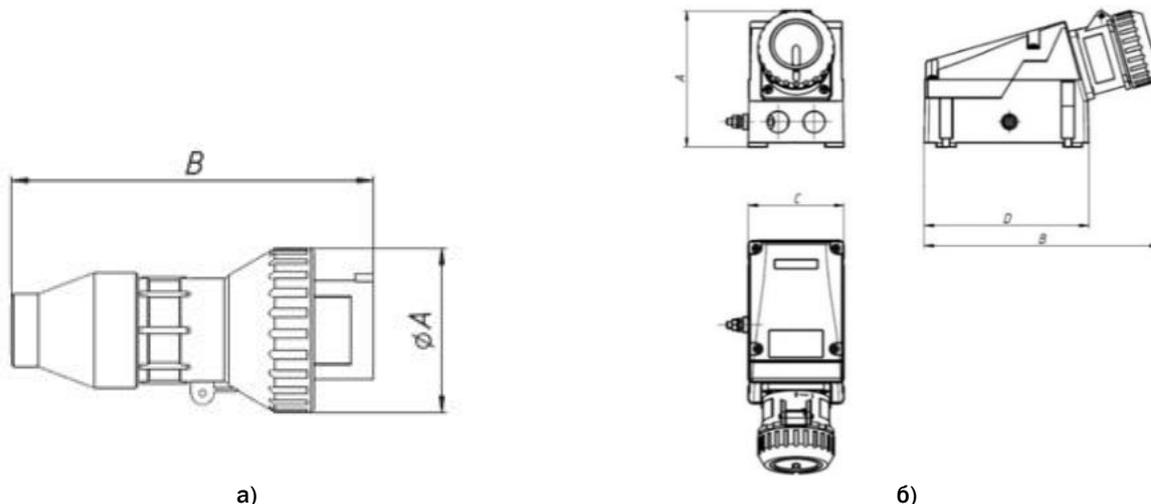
а - Общий вид вилок типа ВГМЕ..., б - Общий вид разъемов типа РГМЕ...
